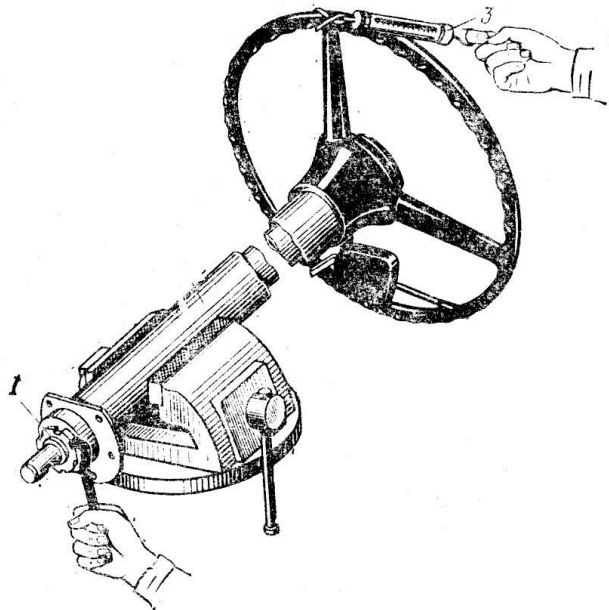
Регулювання підшипників вала рульового колеса автомобіля ЗИЛ-130:
